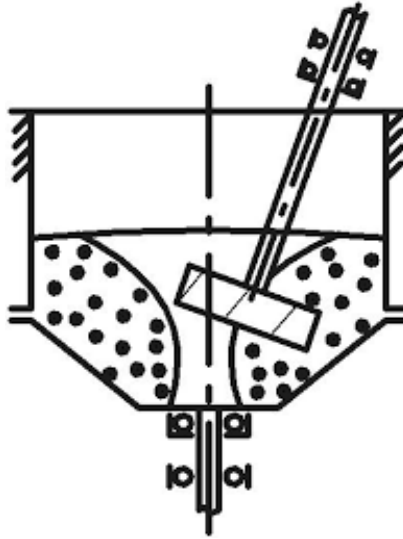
Схема центробіжно-ротаційного оброблення
